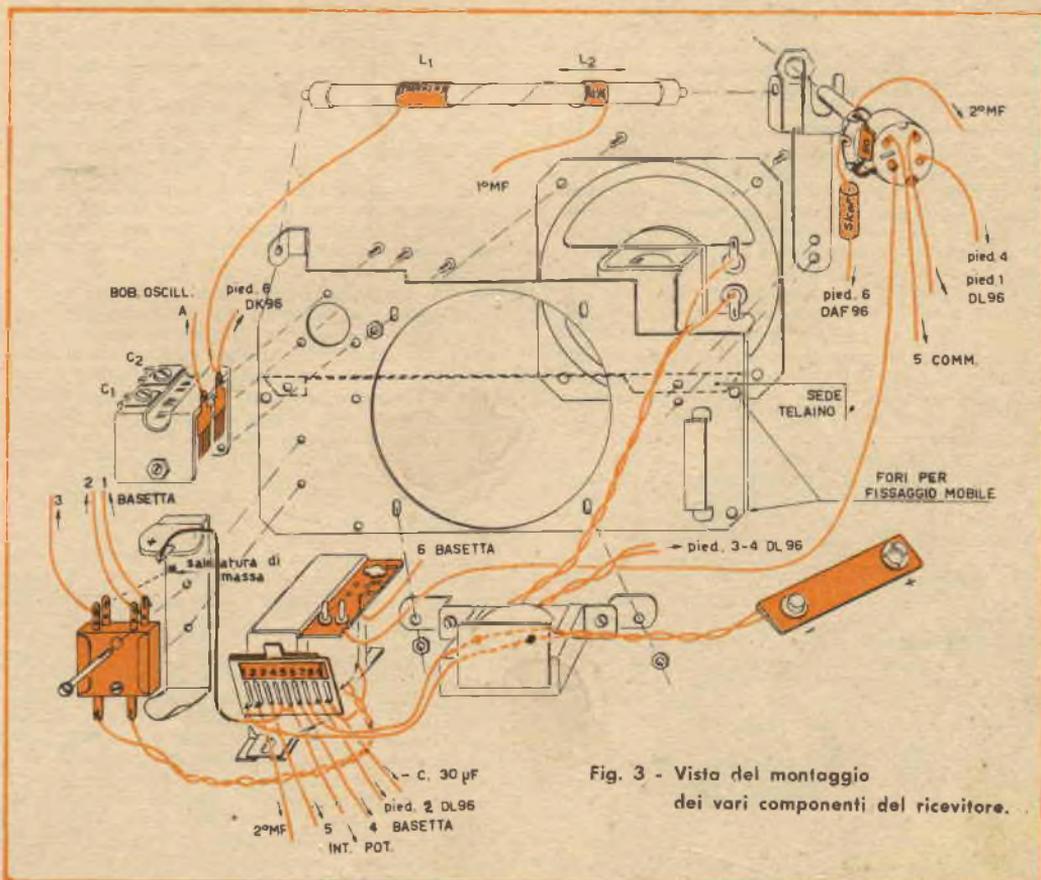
Vista del montaggio dei vari componenti del ricevitore.
